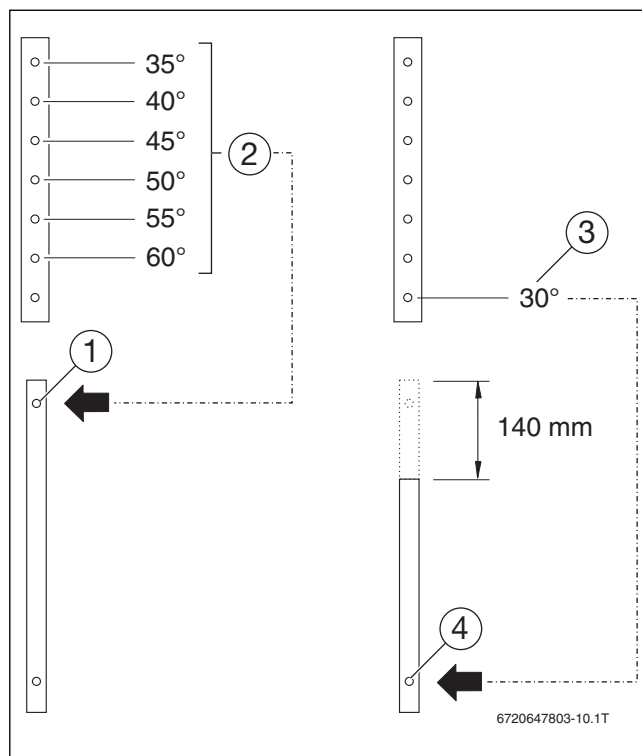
Монтаж телескопічної шини — горизонтальний тип колектора
